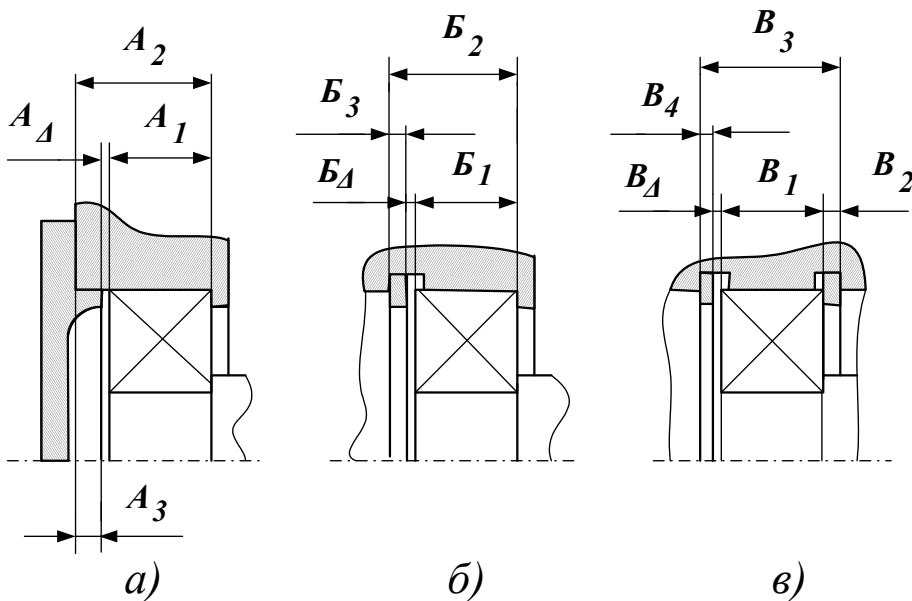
Варианты установки подшипника в корпус и размерные цепи, описывающие возможность сборки подшипниковой опоры и ее нормальной работы
